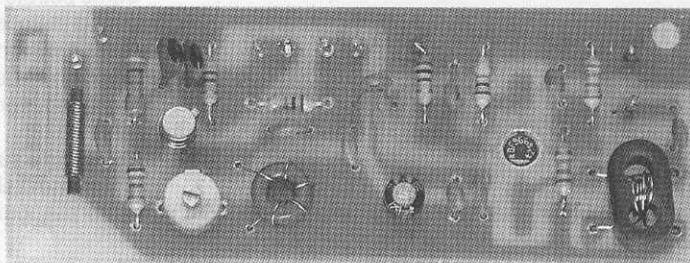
Schema pratico di montaggio dell'LX.1018/B. Il mosfet MFT1 viene montato e saldato sul lato rame del circuito stampato. Il disegno di questo stampato è riprodotto in fig.20.
